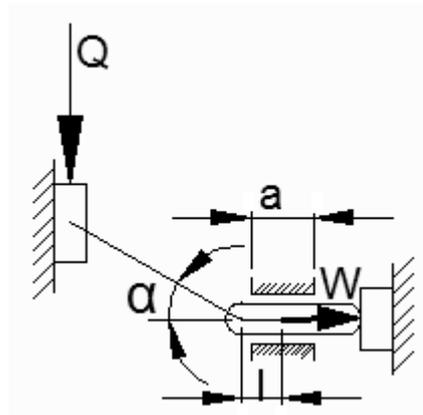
Схема рычажно-шарнирного механизма с консольным плунжером.
